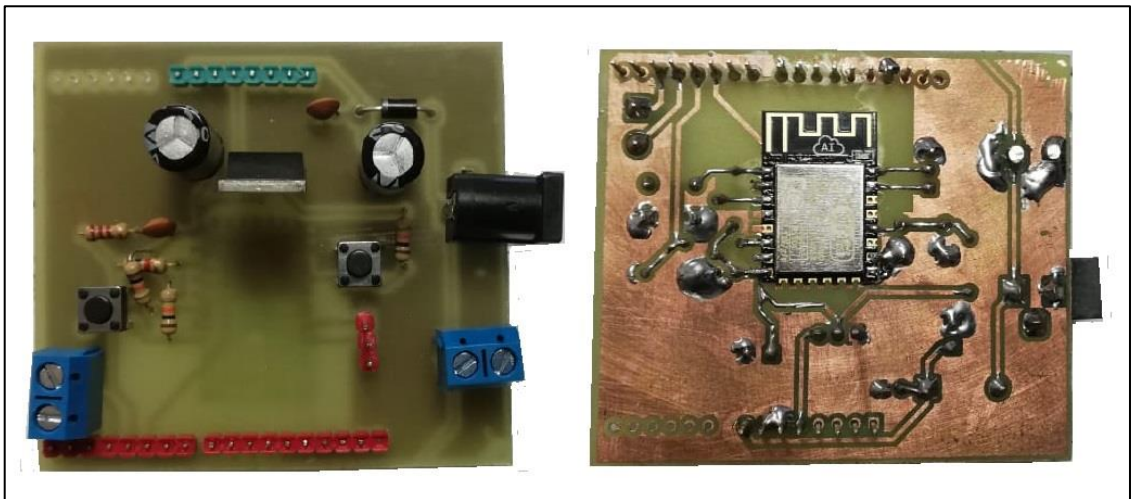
Placa “B” terminada (frontal y reverso)
